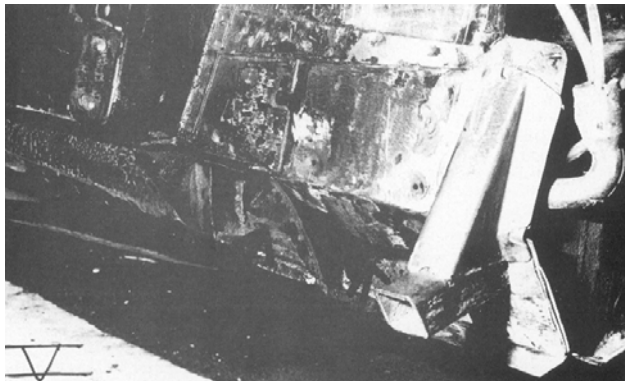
Foto V: Voorzijde onderkant tussen portierophanging en bokjes steun. Dit is hier opengeknipt, u ziet een wederom beruchte holle ruimte. Boor 2 gaaties en stuit goed vol.
